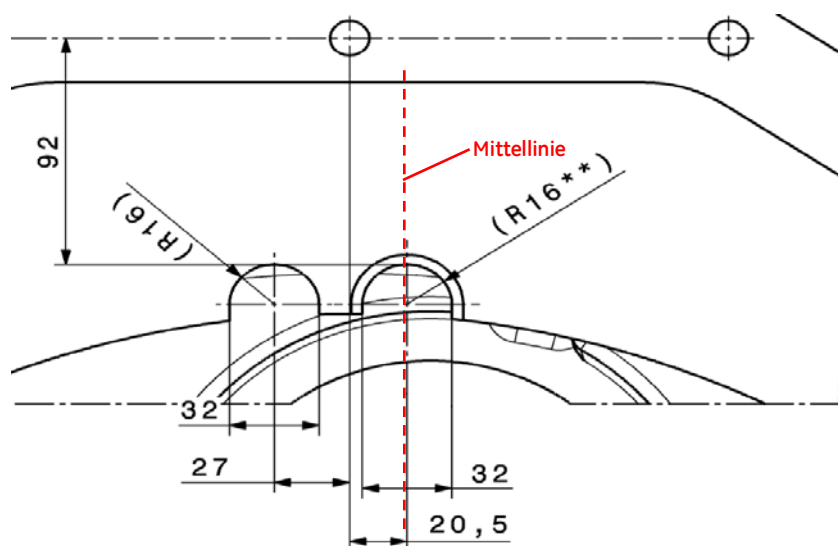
Zeichnungsausschnitt - Ausnehmungen
